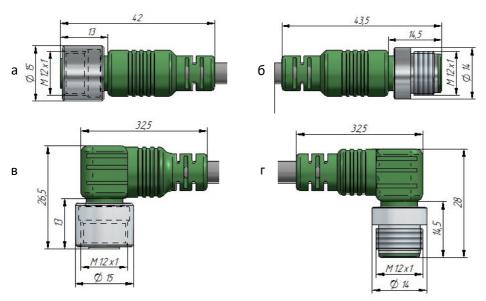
Внешний вид и габаритные размеры соединительных кабелей с одним разъемом: a) прямой розетка, б) прямой вилка, в) угловой розетка, г) угловой вилка
